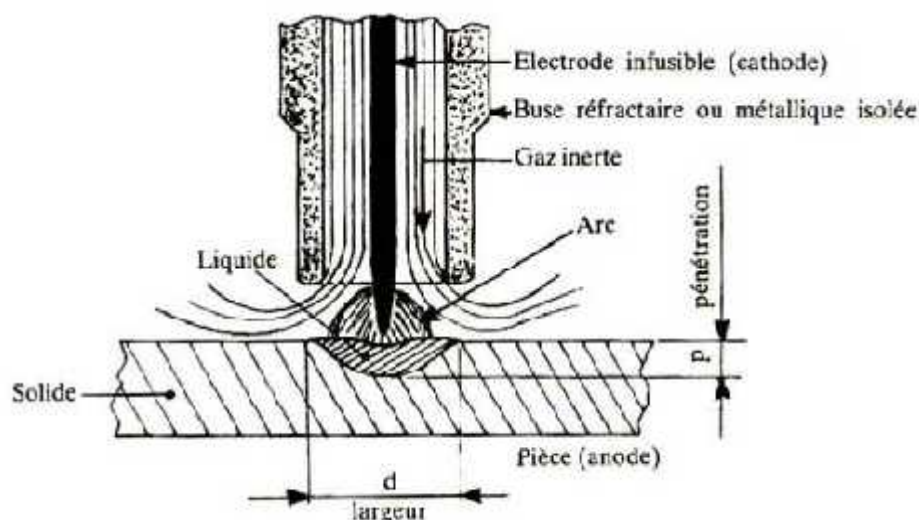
Principe du procédé de soudage TIG simple flux. [1]
